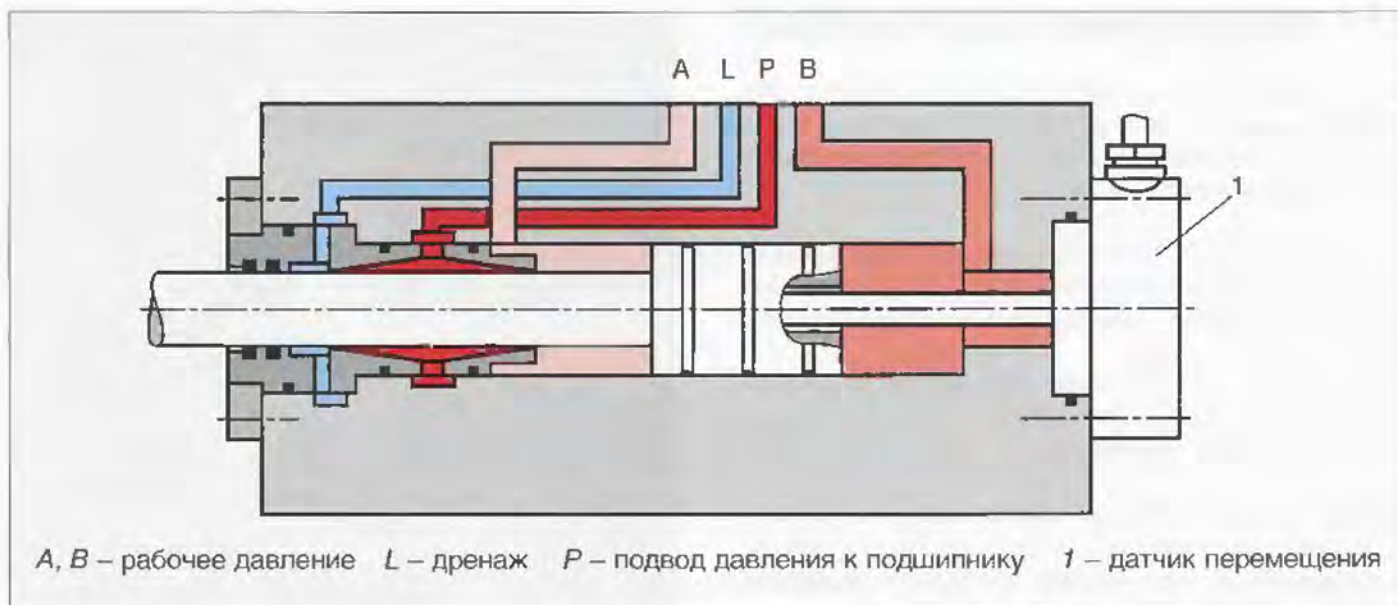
Схема сервоцилиндра с опорой штока в виде гидростатического клинового зазора
